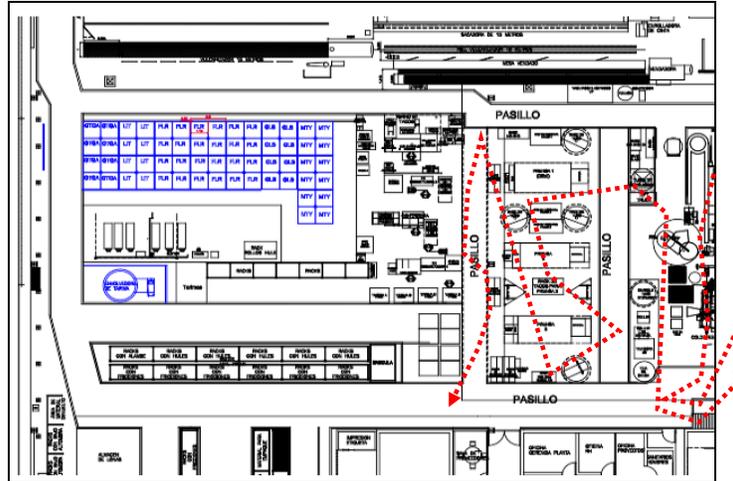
Propuesta 1 de layout (con maquinaria instalada).
